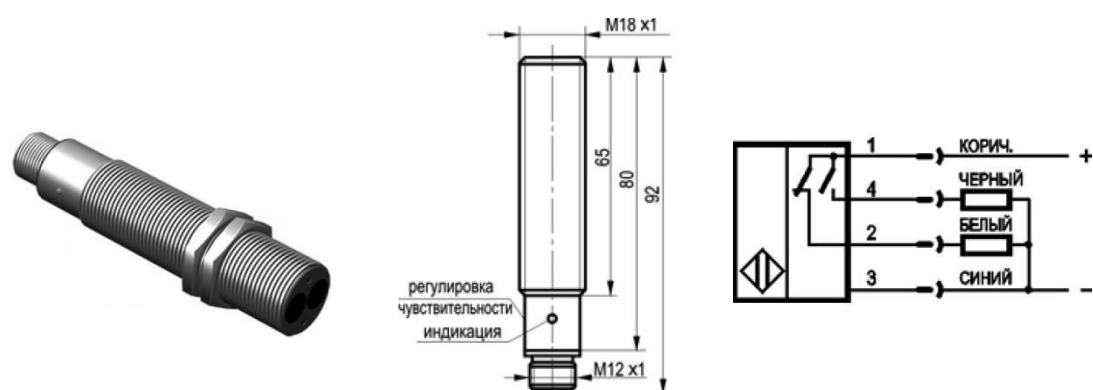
Внешний вид, габаритный чертёж и схема подключения оптического датчика OV AC43A5-43P-R400-LZS4
